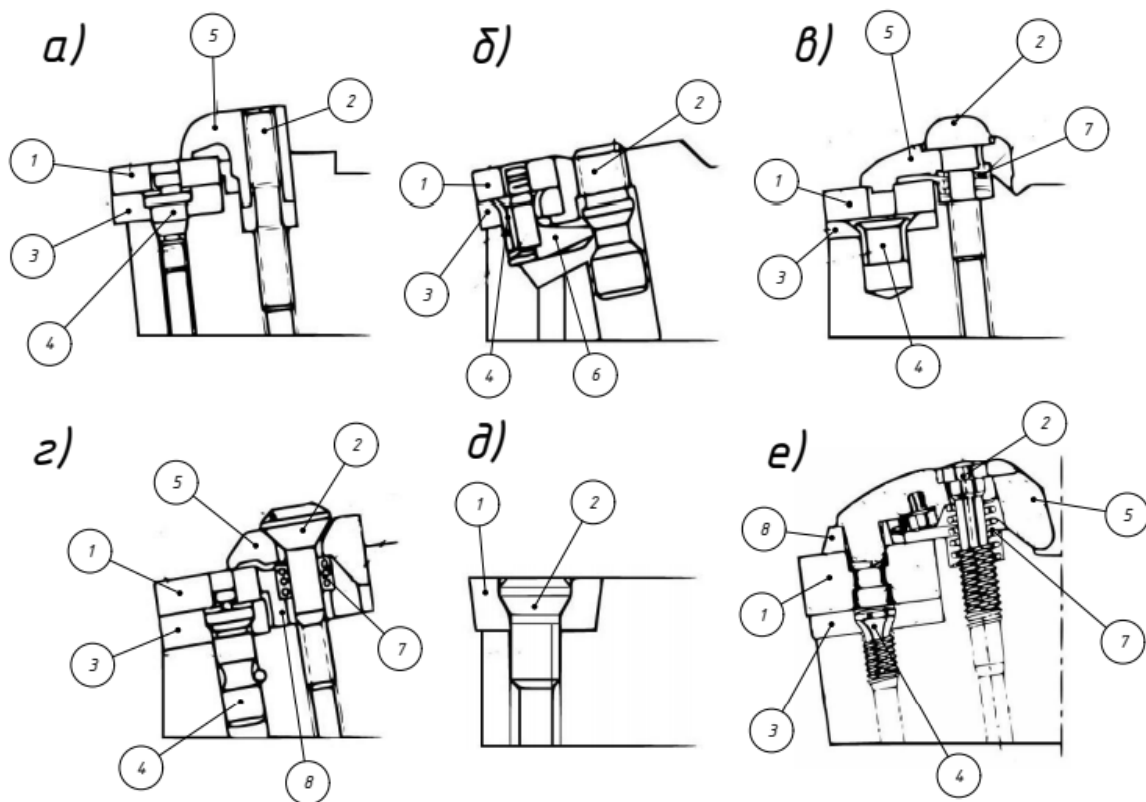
Механічні способи кріплення пластин [21, ст. С007]:
